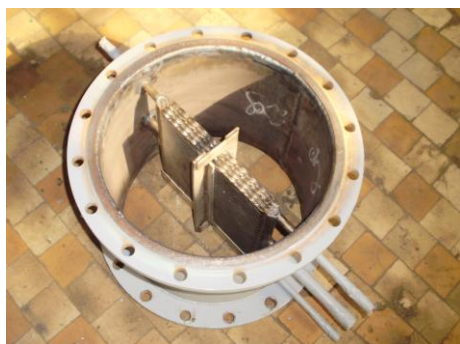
Фрагменты греющей камеры экспериментального выпарного аппарата со сварной пластинчатой греющей камерой
